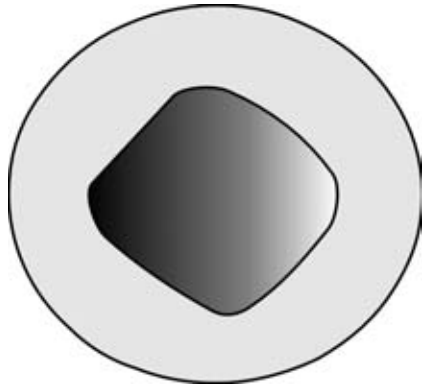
Форма сердцевины в катаной биметаллической заготовке диаметром 90 мм при применении стержня круглого сечения в двухслойном слитке
